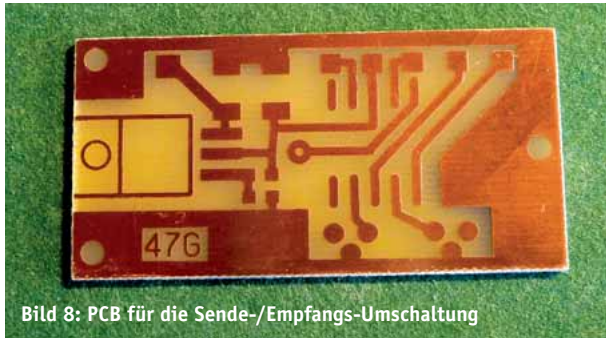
PCB für die Sende-/Empfangs-Umschaltung
